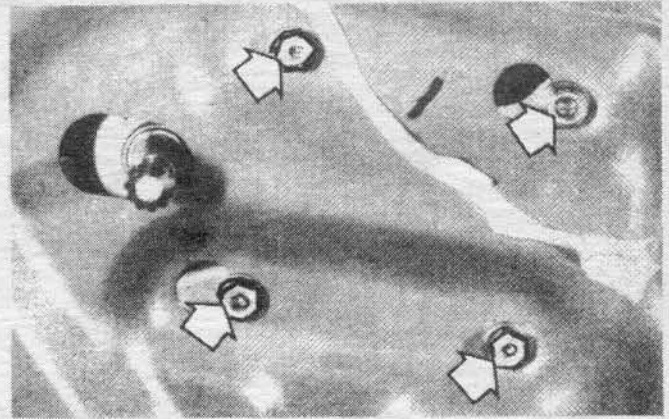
а Болты крепления механизма подъема около ручки стеклоподъемника.
